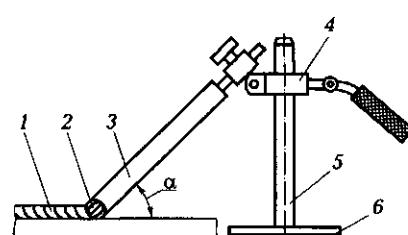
Схема сварки наклонным электродом:
